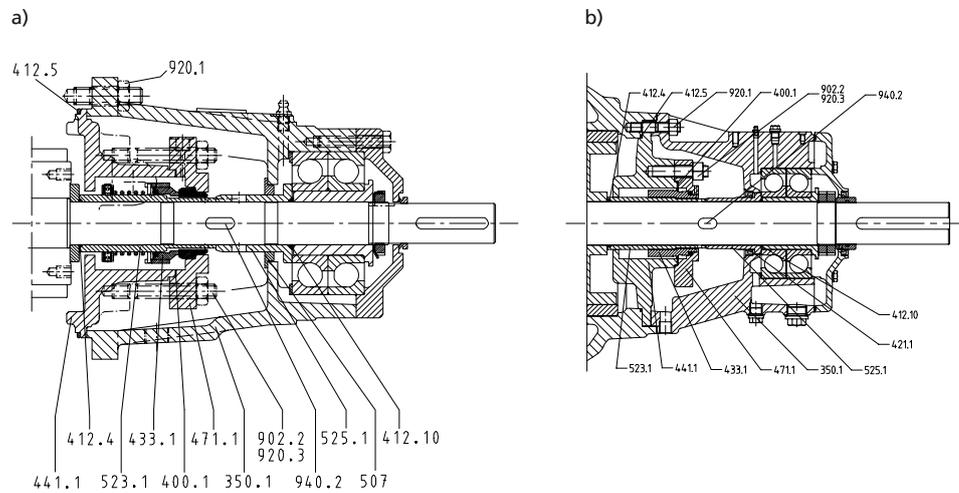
Desmontaje del cierre mecánico: a) Tamaño 32-200 y b) Tamaño 250
